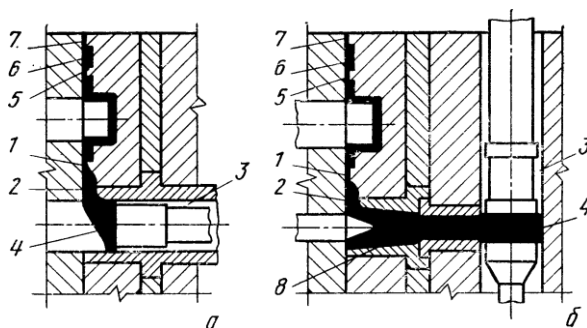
Литниковые системы для литья под давлением на машинах с холодной камерой прессования: *a* – горизонтальной; *б* – вертикальной; 1 – питатель; 2 – переходный канал; 3 – камера прессования; 4 – пресс-остаток; 5 – щель; 6 – промывник; 7 – вентиляционный канал; 8 – литниковый ход
